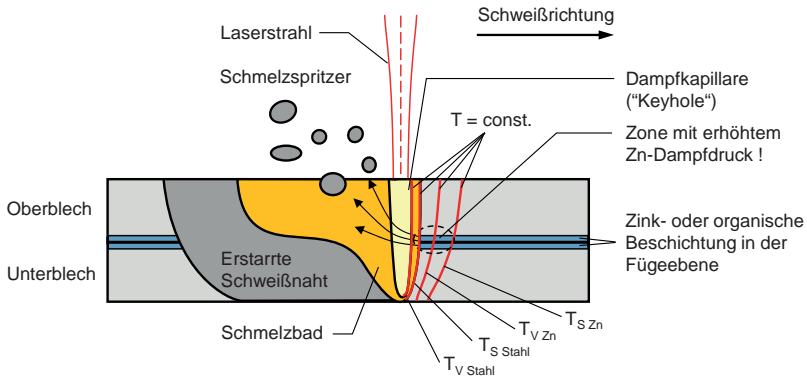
Grundproblematik der Entgasung beim Laserstrahlschweißen zinkbeschichteter Stahlbleche im Überlapstoß. Bei Nullspaltschweißungen entweicht der Zinkdampf über die Schmelze – Auswürfe sind die Folge.
